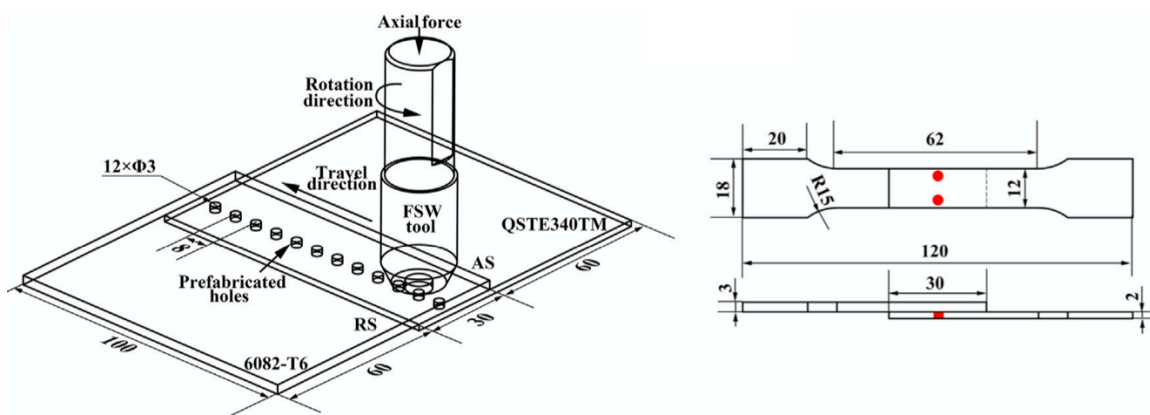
Configuración soldadura solapada con taladros propuesta por Huang et al. [78]
